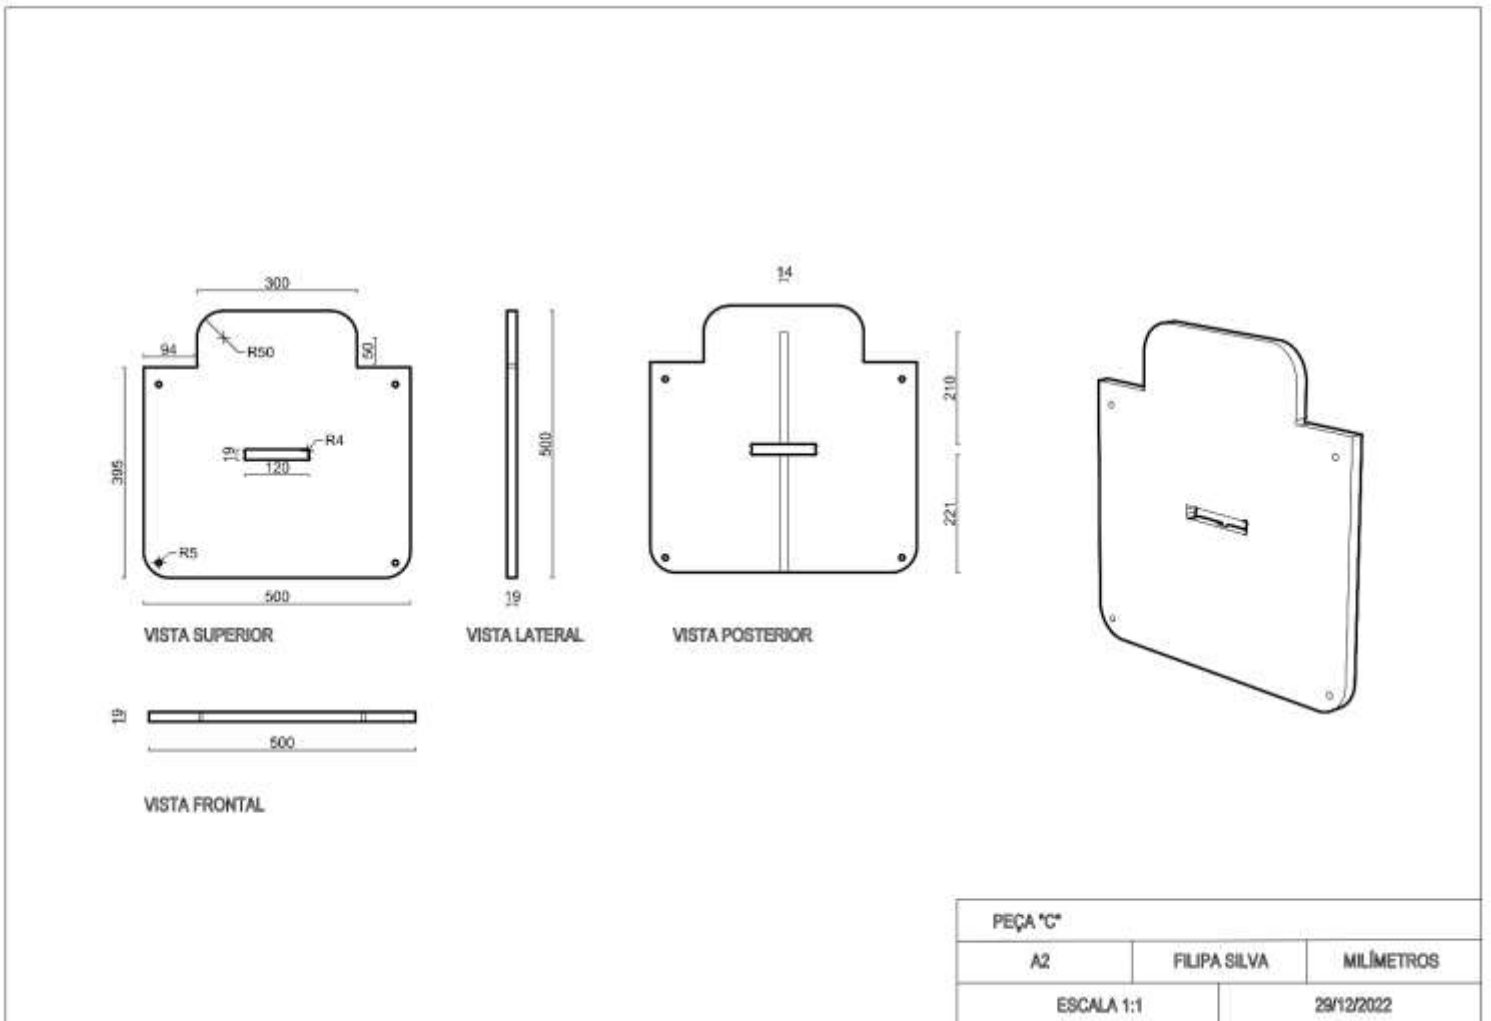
Desenho técnico peça "C" (Fonte: o autor)
